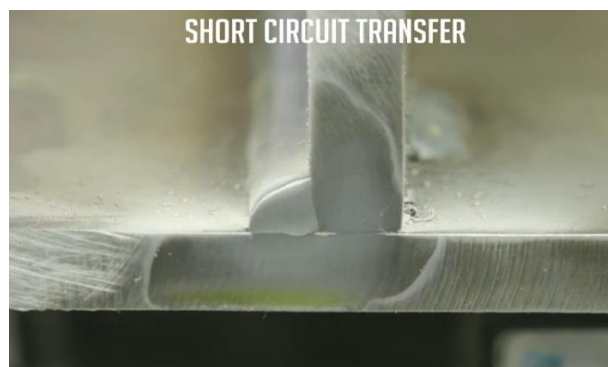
Розріз зварного шва, виконаного в режимі переносу металу коротким замиканням
